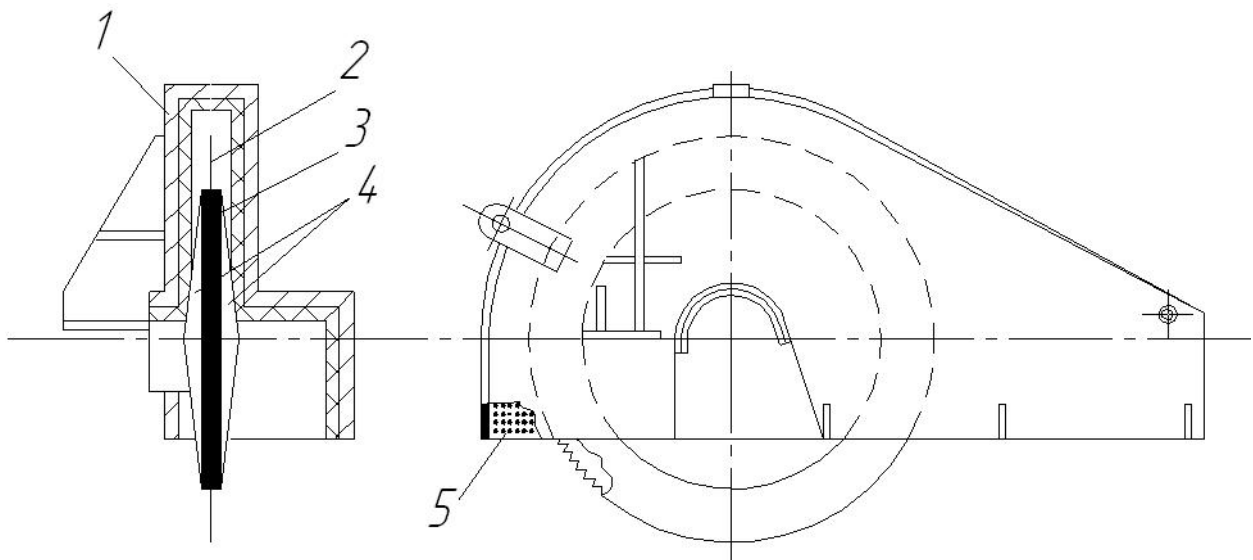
Пристрій для глушіння шуму дискової пилки:
